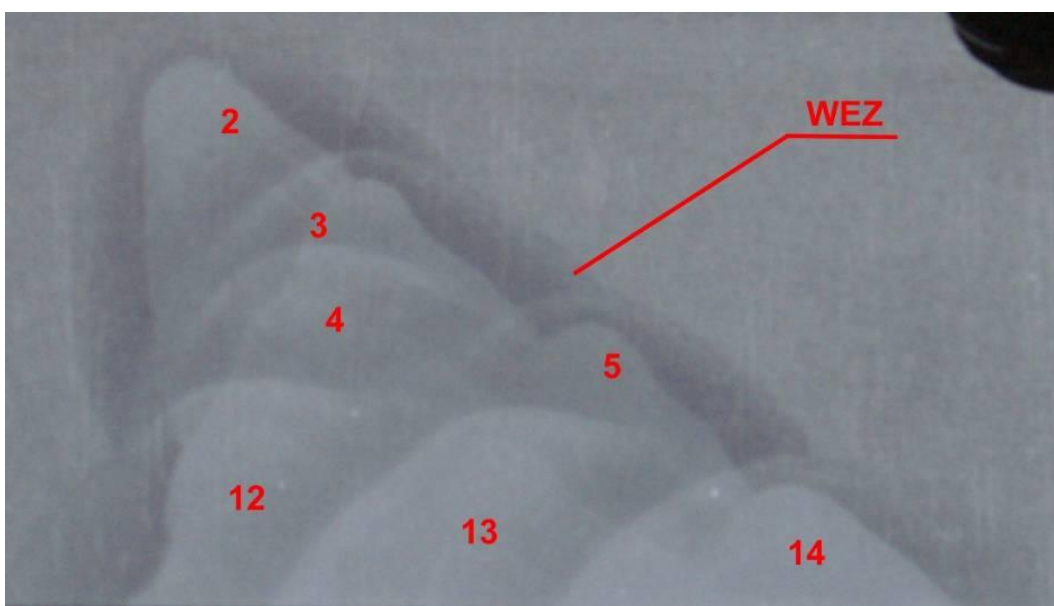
Probe 04 - Ansicht unterer Teil der Schweißnaht
